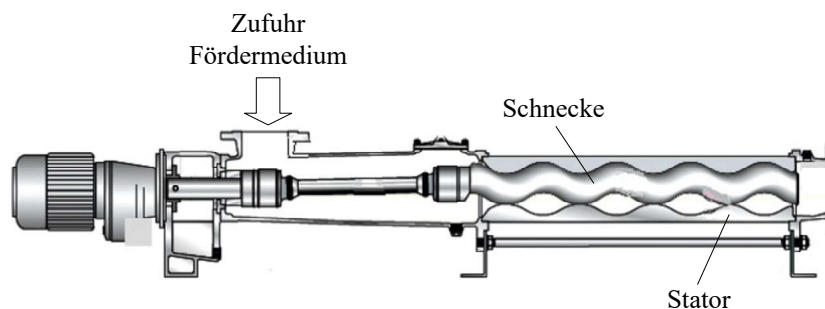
Prinzipieller Aufbau einer Exzentrerschneckenpumpe [66]
